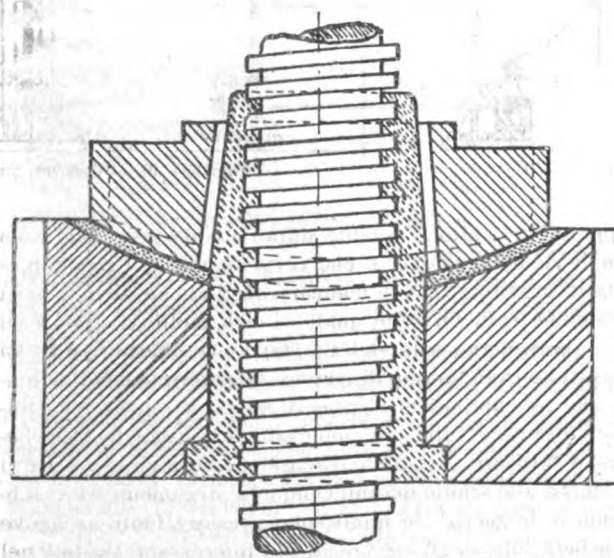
Cavalletti Schlesinger - Sezione della chiocciola.
